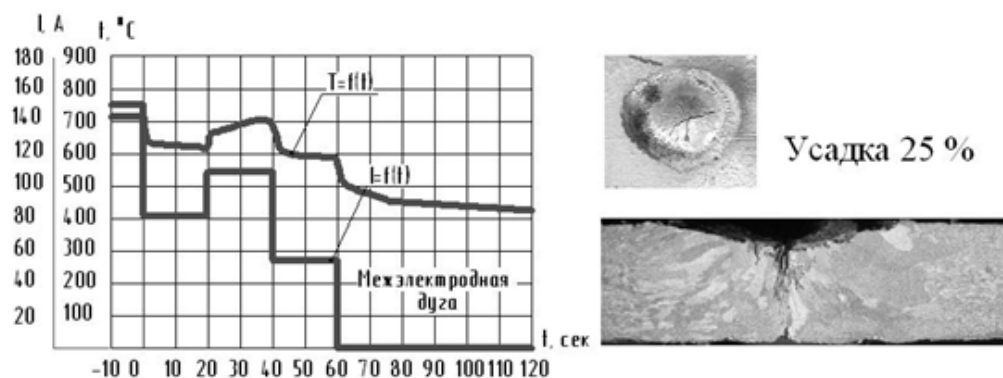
Термический цикл, форм и размеры усадочного кратера при реализации обратно ступенчатой формы кривой спада тока сварки
